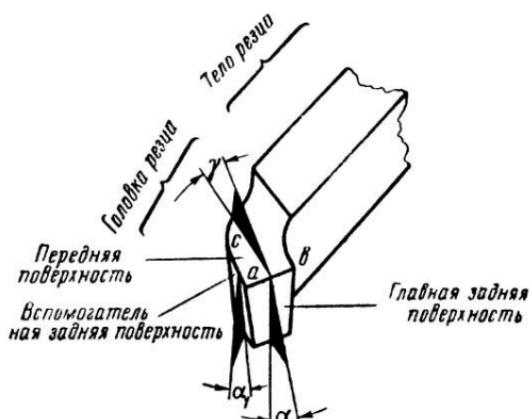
Основные углы резца и его элементы. a — вершина резца; av — главная режущая кромка; ac — вспомогательная режущая кромка; α — задний угол у главной режущей кромки, α_1 — задний угол у вспомогательной режущей кромки; γ — передний угол.
